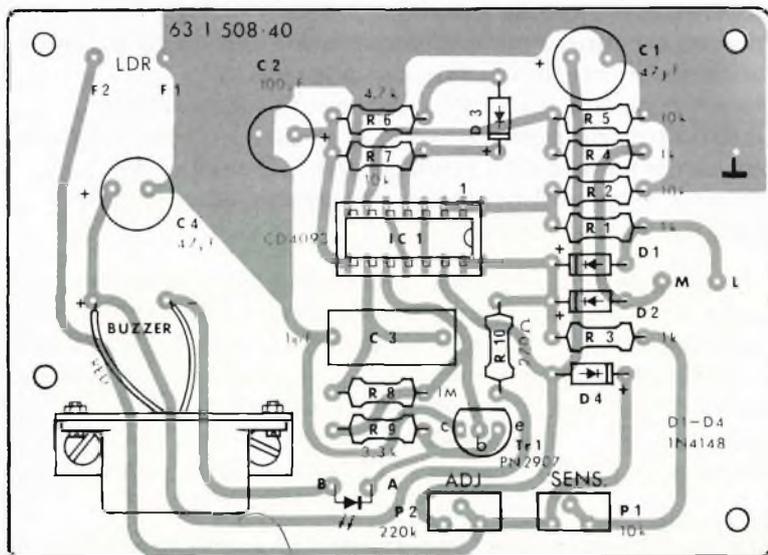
Circuito stampato lato-componenti con veduta in trasparenza del lato-rame
